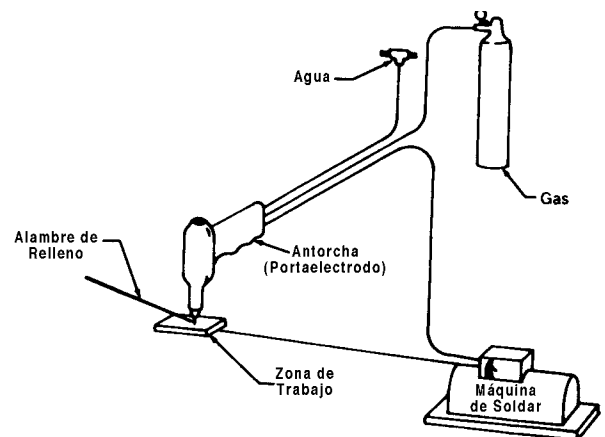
Soldadura por Arco de Tungsteno en Atmósfera Inerte (MIG)
